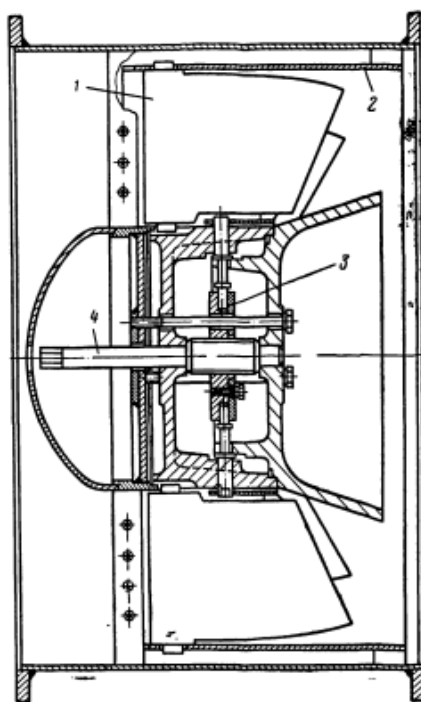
Направляющий аппарат вентилятора ВМ-6М: 1 — лопатка направляющего аппарата; 2 — обечайка; 3 — механизм поворота лопаток направляющего аппарата; 4 — винтовой валик
